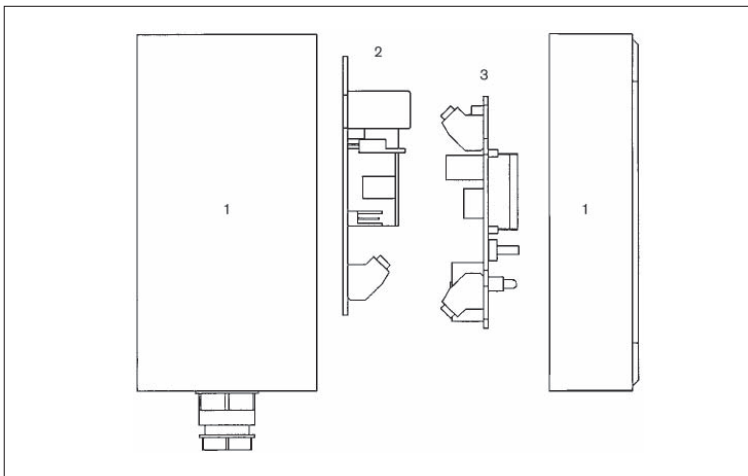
Ersatzteil-Explosionszeichnung, Ausführung für Schaltschrankmontage
